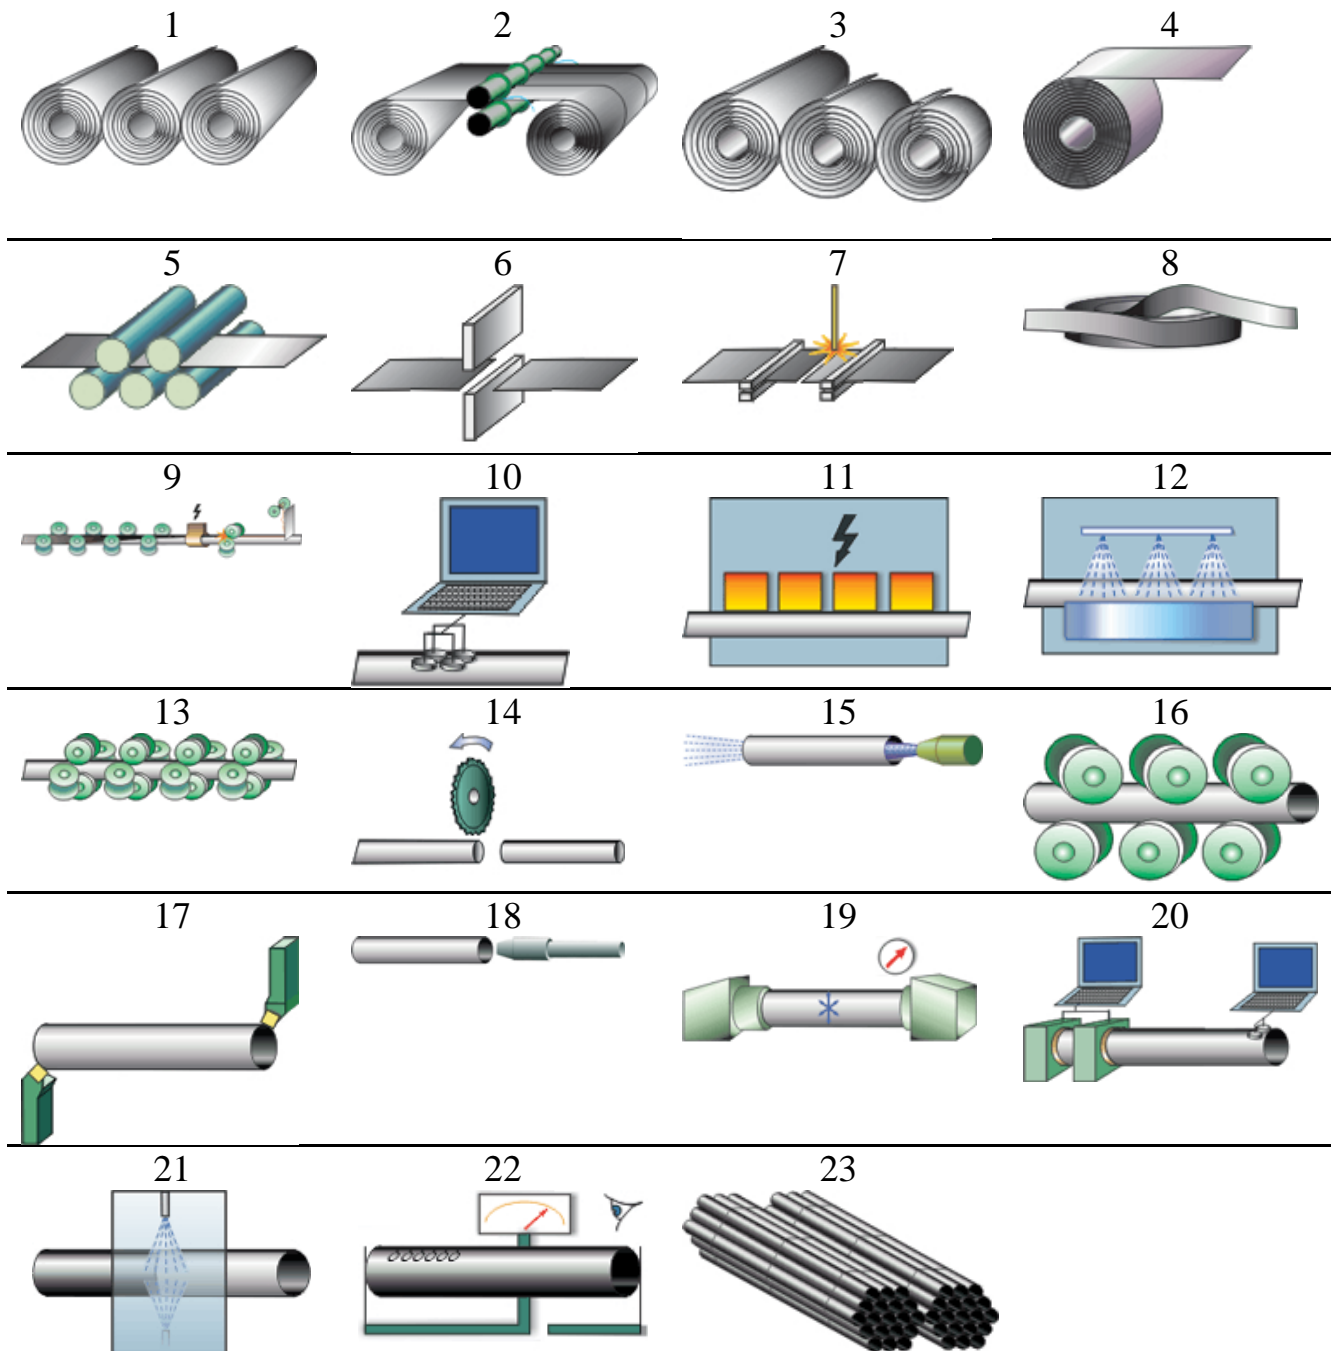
Формовочное и сварочное оборудование
